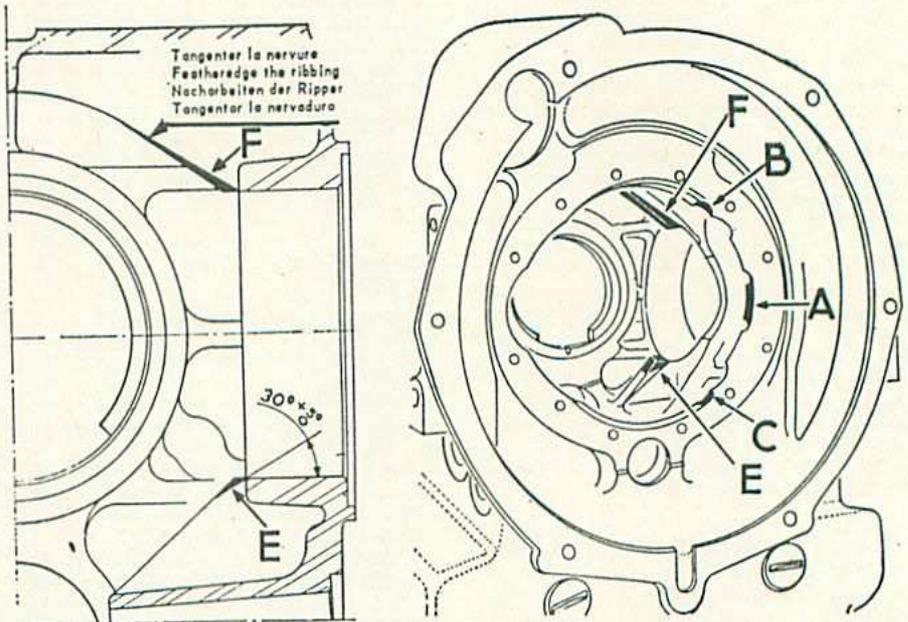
Retouches de certains carters pour montage du vilebrequin n° 354135
